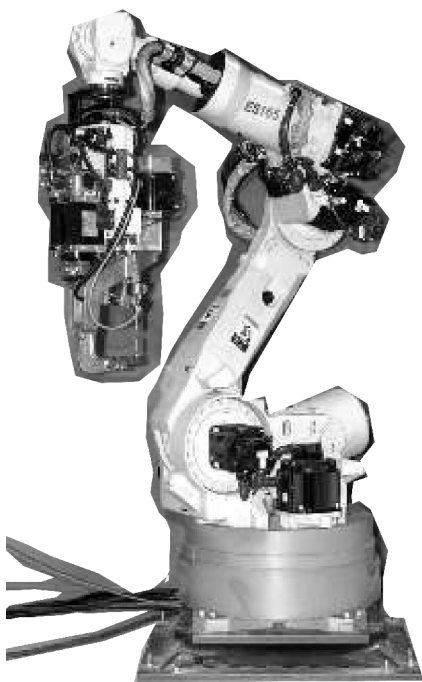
铜合金异型截面结构 C 型焊钳
